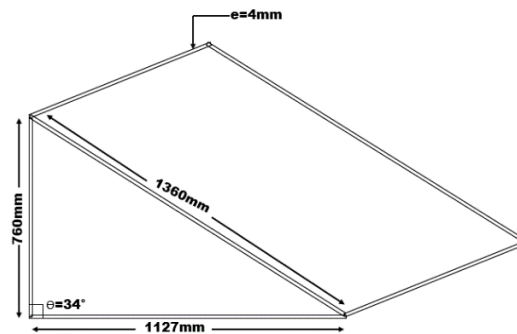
Dimensions du support métallique pour le nouveau module.
